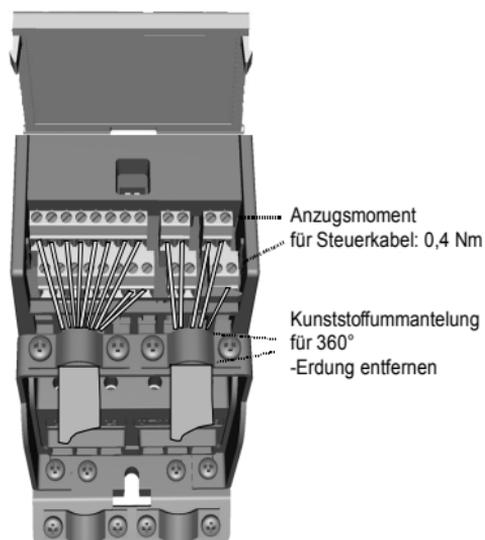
Installieren der Steuerkabel, MI1 - MI3
